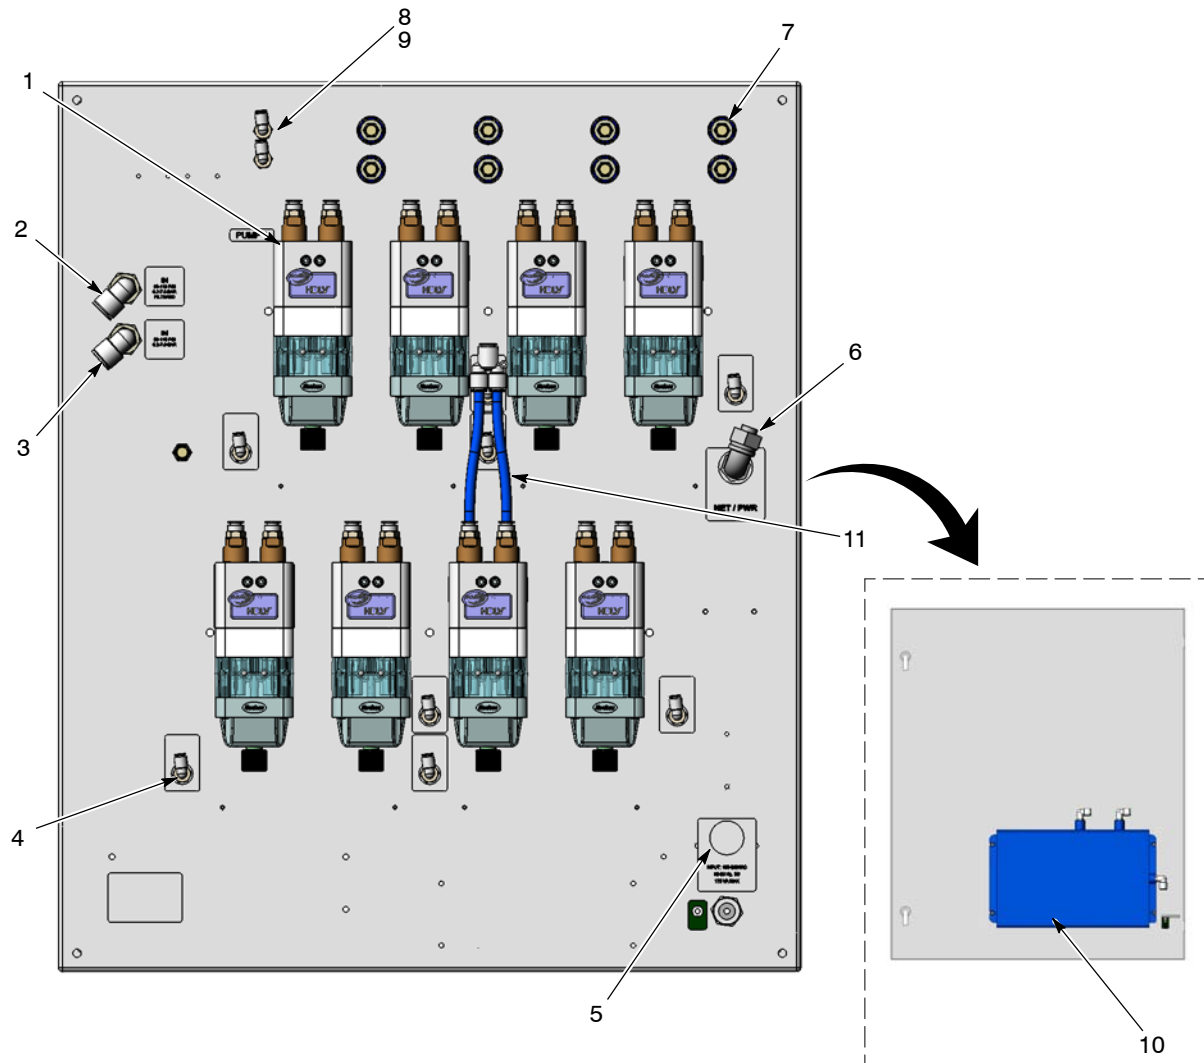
Componenti esterni del pannello pompa (nell'immagine il pannello ad otto pompe)
